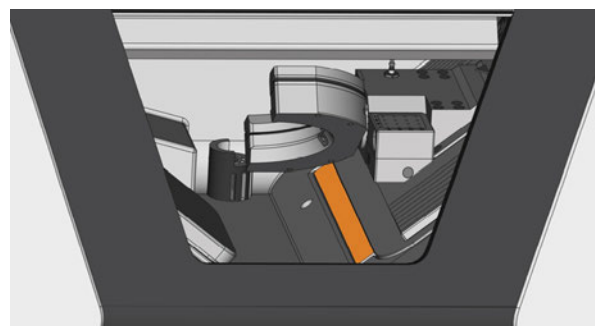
BANDE DE PROTECTION CORRECTEMENT INSTALLÉE (MARQUÉE EN ORANGE)
